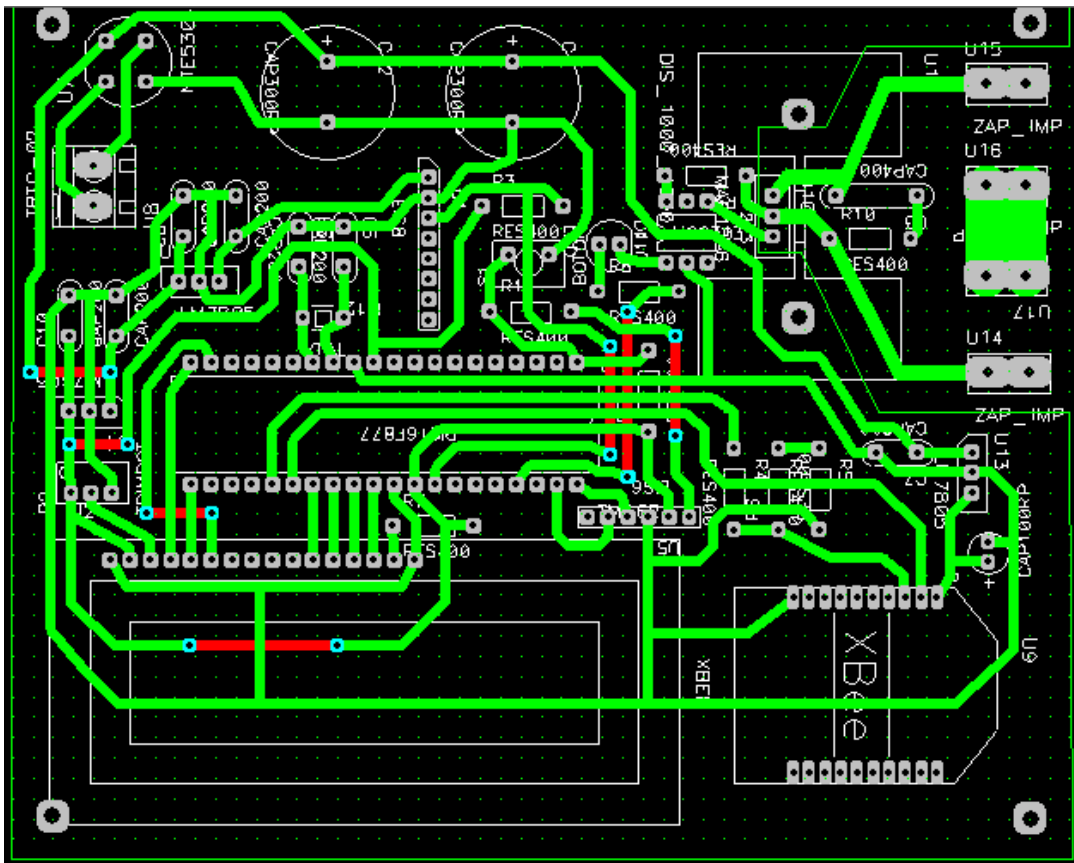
diseño del circuito impreso en la aplicación PCB de P-CAD.
